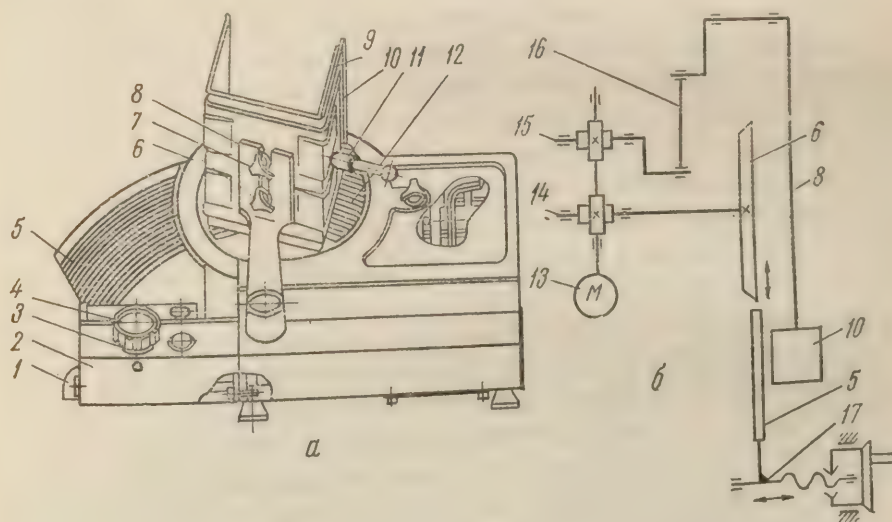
Машина МРГ-300А для нарезки гастрономических товаров:
